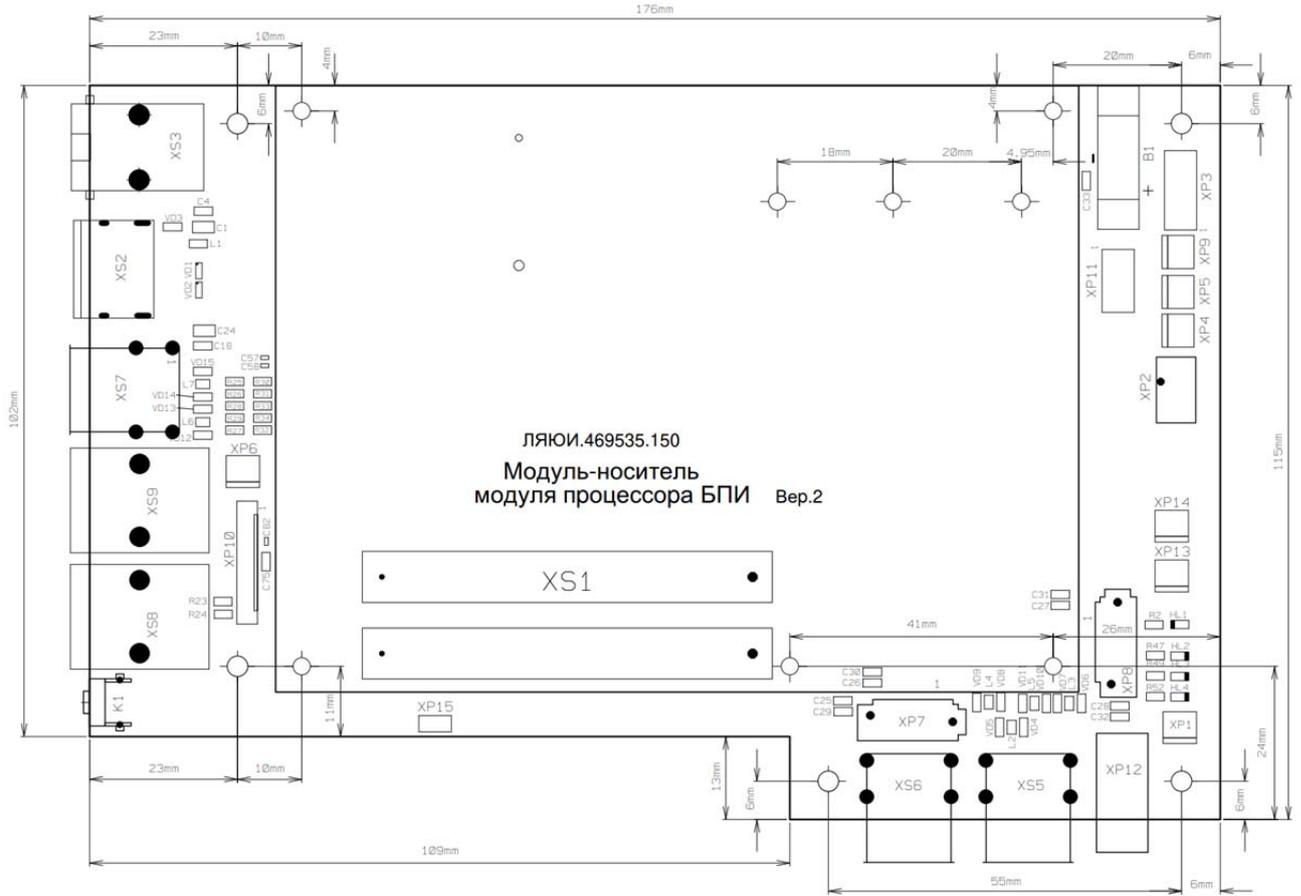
Внешний вид МНМП-БПИ (вид сверху)
